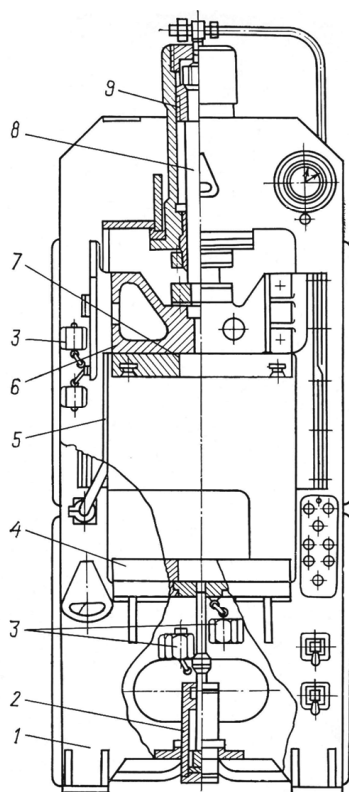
Гидравлический пресс рамной конструкции с верхним расположением рабочего цилиндра:
